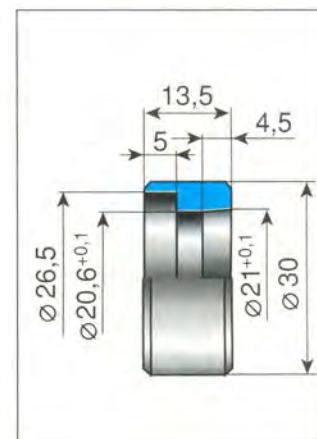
Направляющая втулка для запрессовки поршня в цилиндр.
